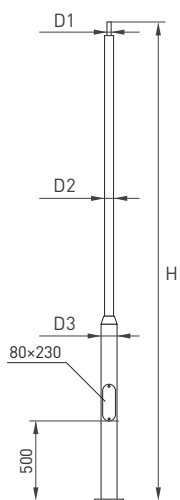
Чертеж и габаритные размеры OXOR-OT2/OK2-D108
